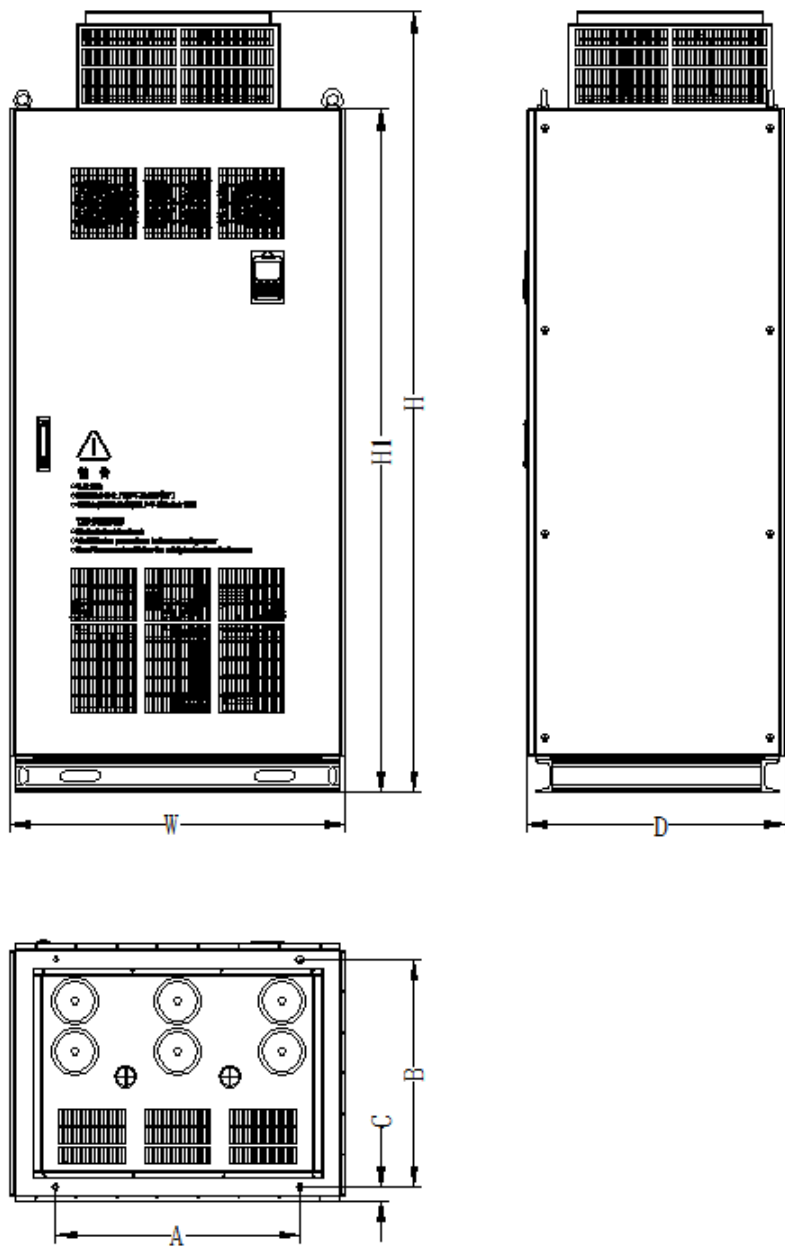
500~630kW 外型尺寸及安装尺寸示意图
